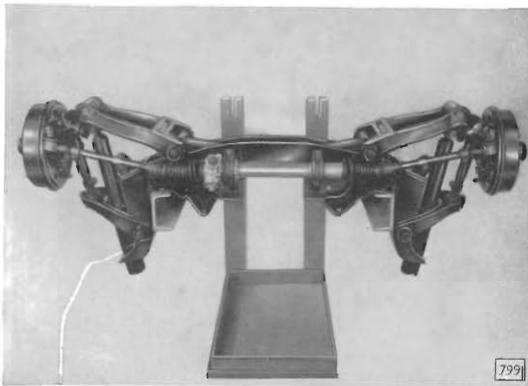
Vorderachse umgekehrt auf Montagebock geschraubt
